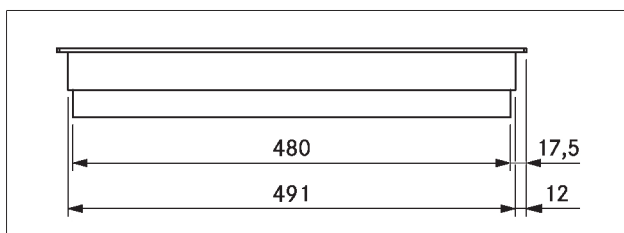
CKCH apparatets dimensjoner sett fra siden
